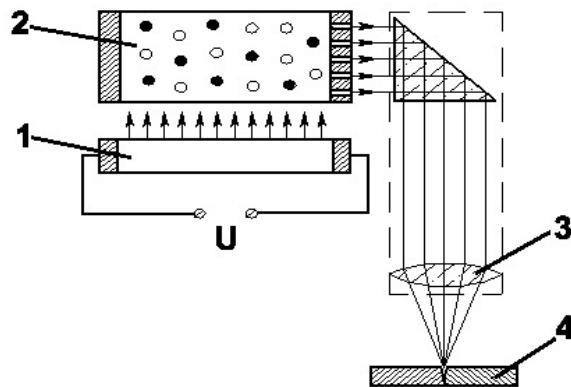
Схема герметизации корпусов лазерной сваркой
